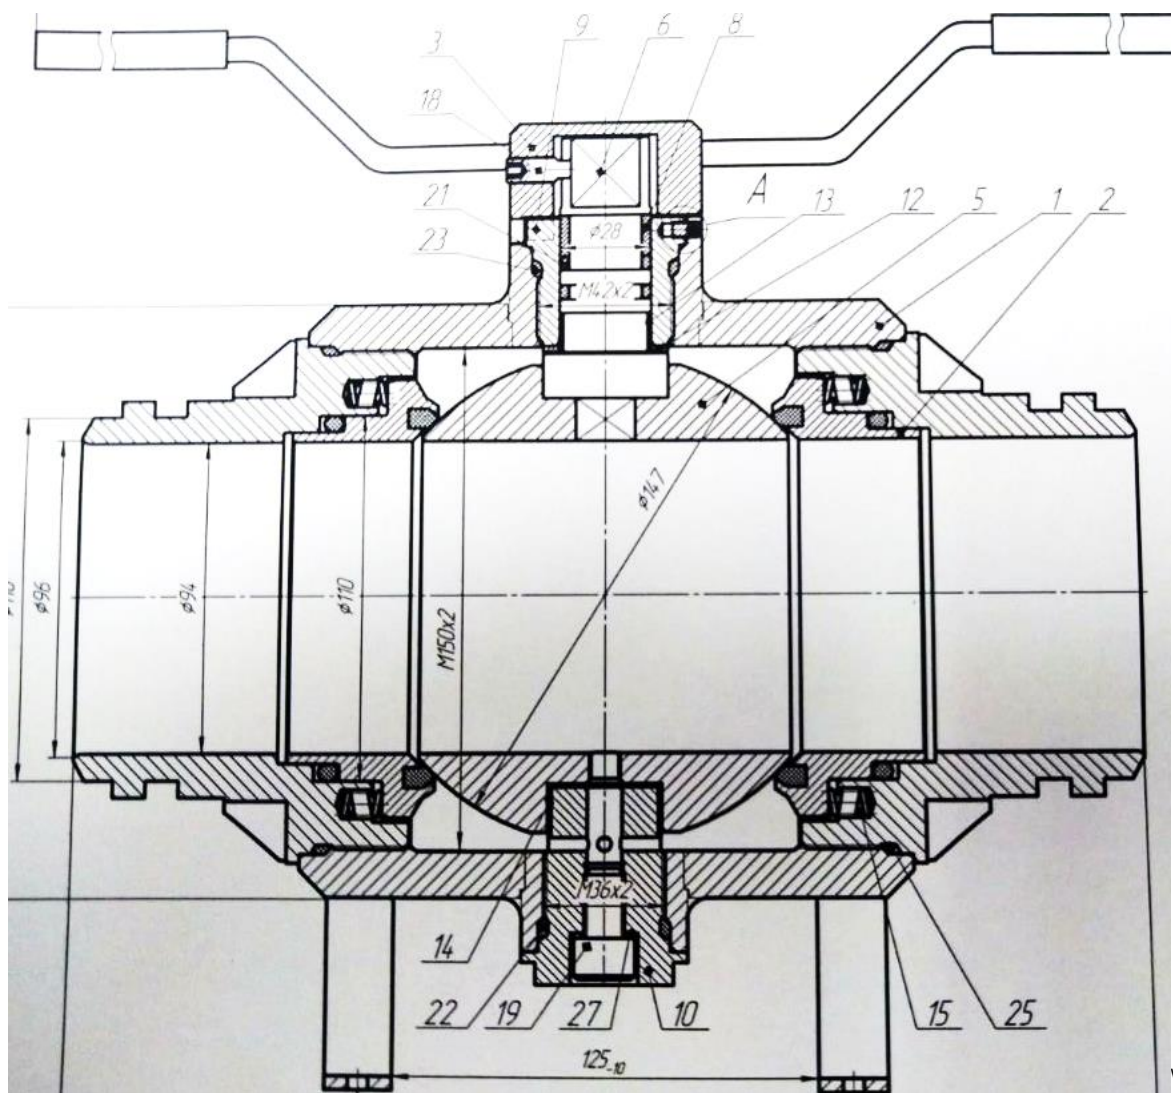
Шаровий кран ДУ100: 1 – Корпус; 2 – Сідло; 3 – Рукоятка; 5 – Пробка; 6 – Шпіндель; 7 – Патрубок; 8 – Кільце; 9 – Штуцер; 10 – Опора; 12 – Підшипник верхній; 13 – Підшипник МФЛ; 14 – Підшипник МФЛ; 15 – Пружина; 16 – Лапа; 17 – Гвинт установчий М5х8; 18 – Гвинт установчий М8х20; 19 – Гвинт М12х20; 21,22,23,24,25 – Кільця ГОСТ 18829 – 73; 27 – Шайба.
